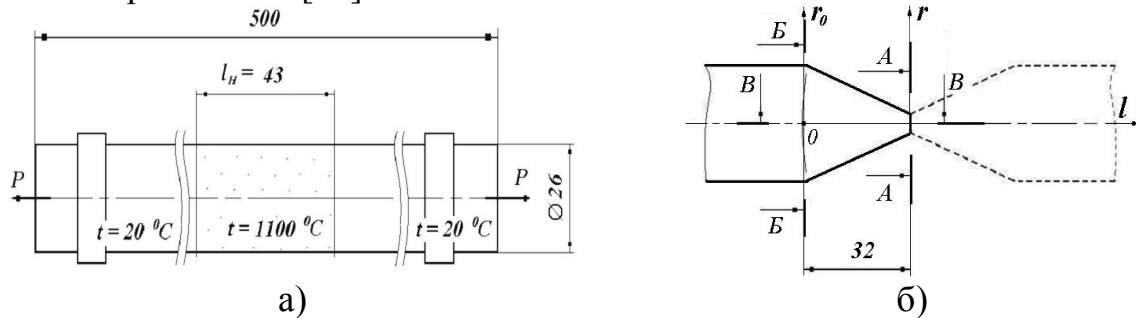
Схема к модели разрыва заготовки для получения поковки «зубило» до деформирования (а) и в момент разделения (б)
